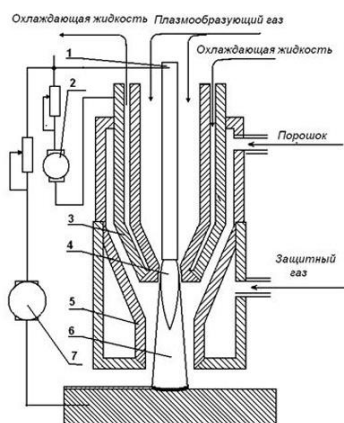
Схема плазменной наплавки с подачей порошкового материала в дугу.
